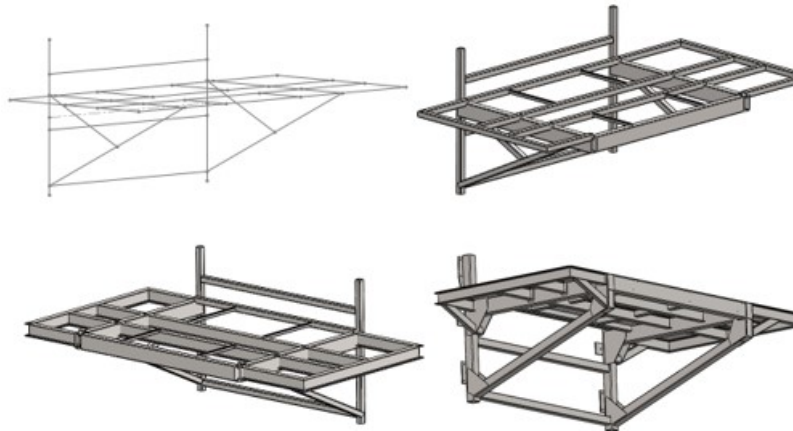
Evolução da construção da estrutura da cesta da plataforma elevatória
